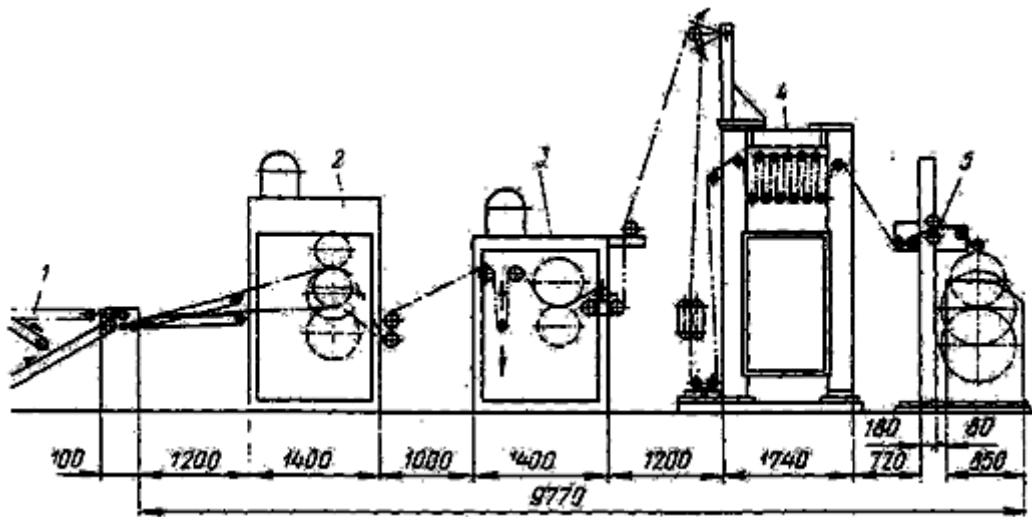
Агрегат фірми «Бабкок» для виготовлення НТМ за способом термобондінг:
